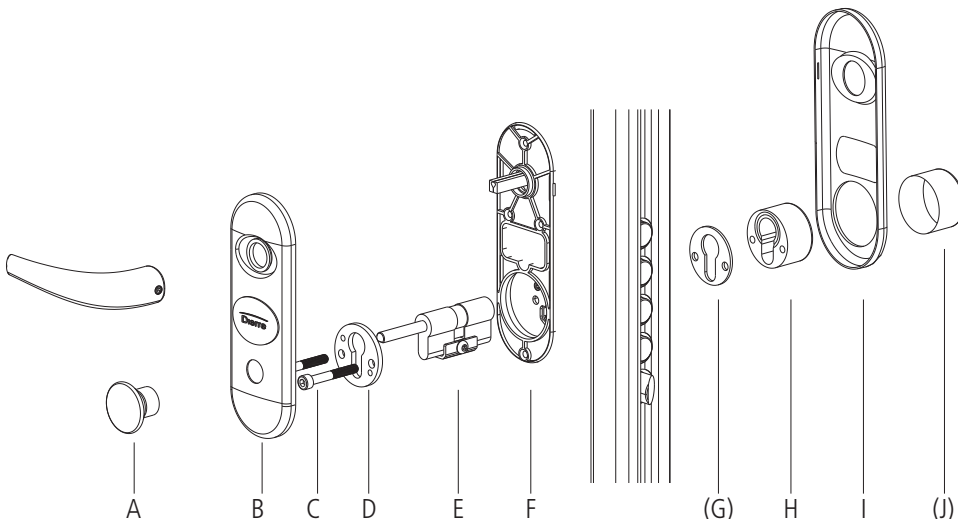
Préparation du barillet pour serrure à engrenages.
